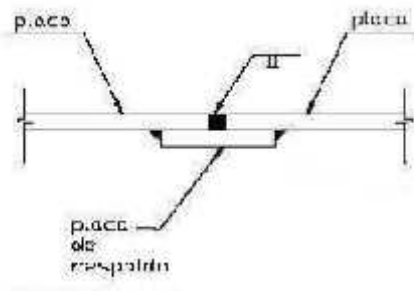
Soldadura a tope simple con respaldo ¹²
